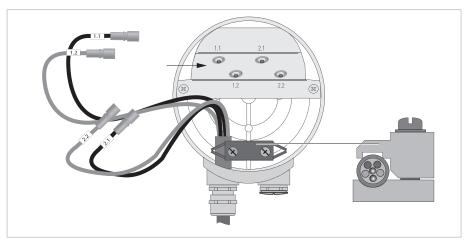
Conecte los cables en la caja de conexión del sensor de caudal
